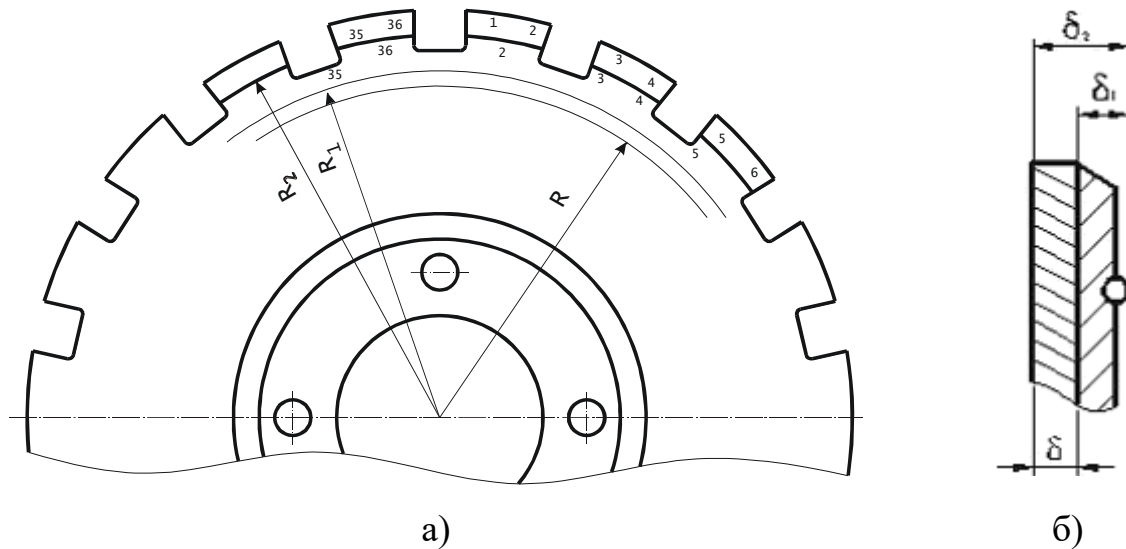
а – диск культиватора, підготовлений для вимірювання товщини наплавленого металу і деформації [14]; б – переріз в зоні наплавлення
